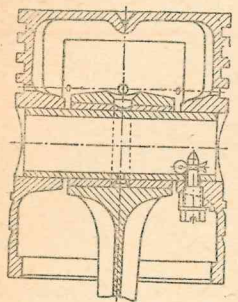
Поршень двигателя СТЗ—ХТЗ для жидкого топлива
